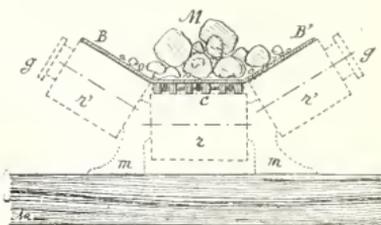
Coupe verticale et plan d'un transporteur à courroies (Getting et Jonas).
